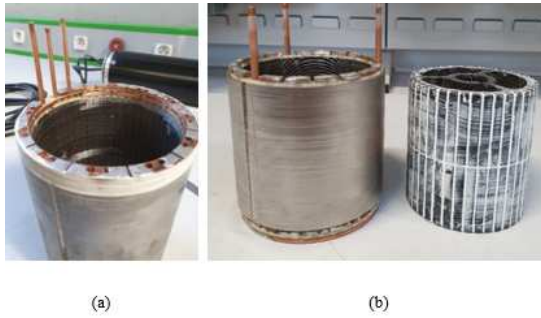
a) stator du moteur M-R, b) stator et rotor du moteur M-Q
